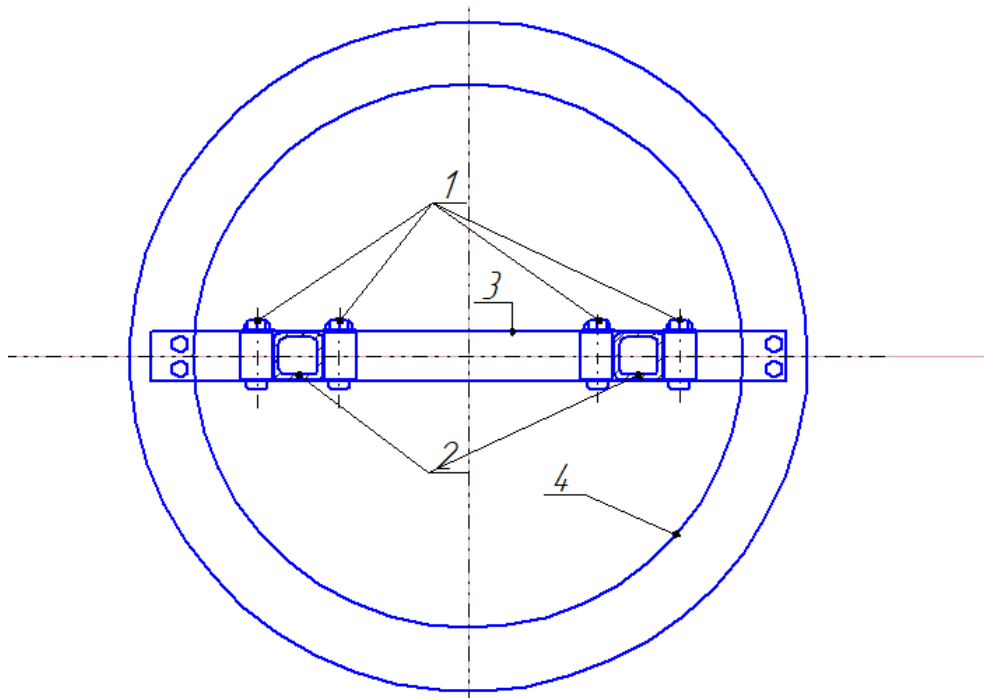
Оборотний обод з рейкою та фіксаторами
